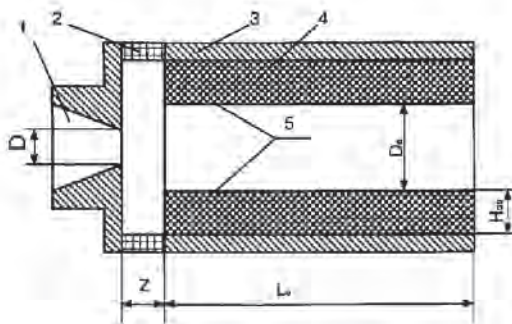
Расчетная схема реактивного глушителя шума эжекторного типа, состоящего из сопла 1, прикрепленного к корпусу 3 глушителя с зазором «Z» через акустически прозрачное кольцо 2, звукопоглощающей вставки 4 с акустически прозрачной пленкой 5.
